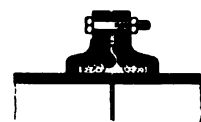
wie Fig. 115. (Dingl. polyt. Journ. 1886, S. 534.)
